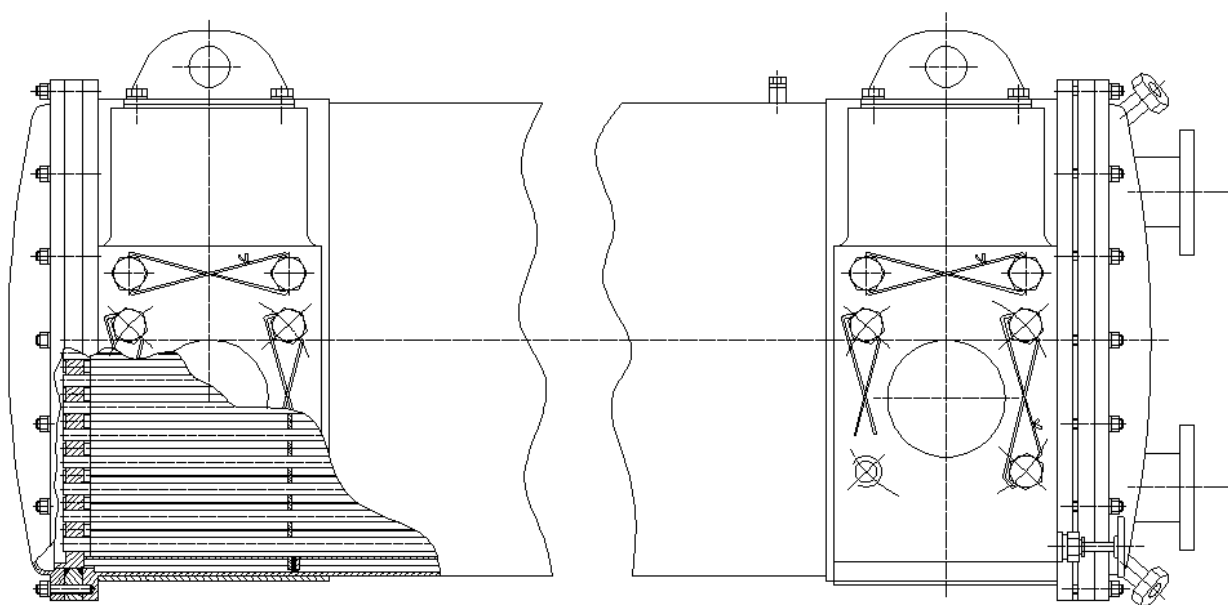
Загальний вид кожухотрубного маслоохолоджувача
